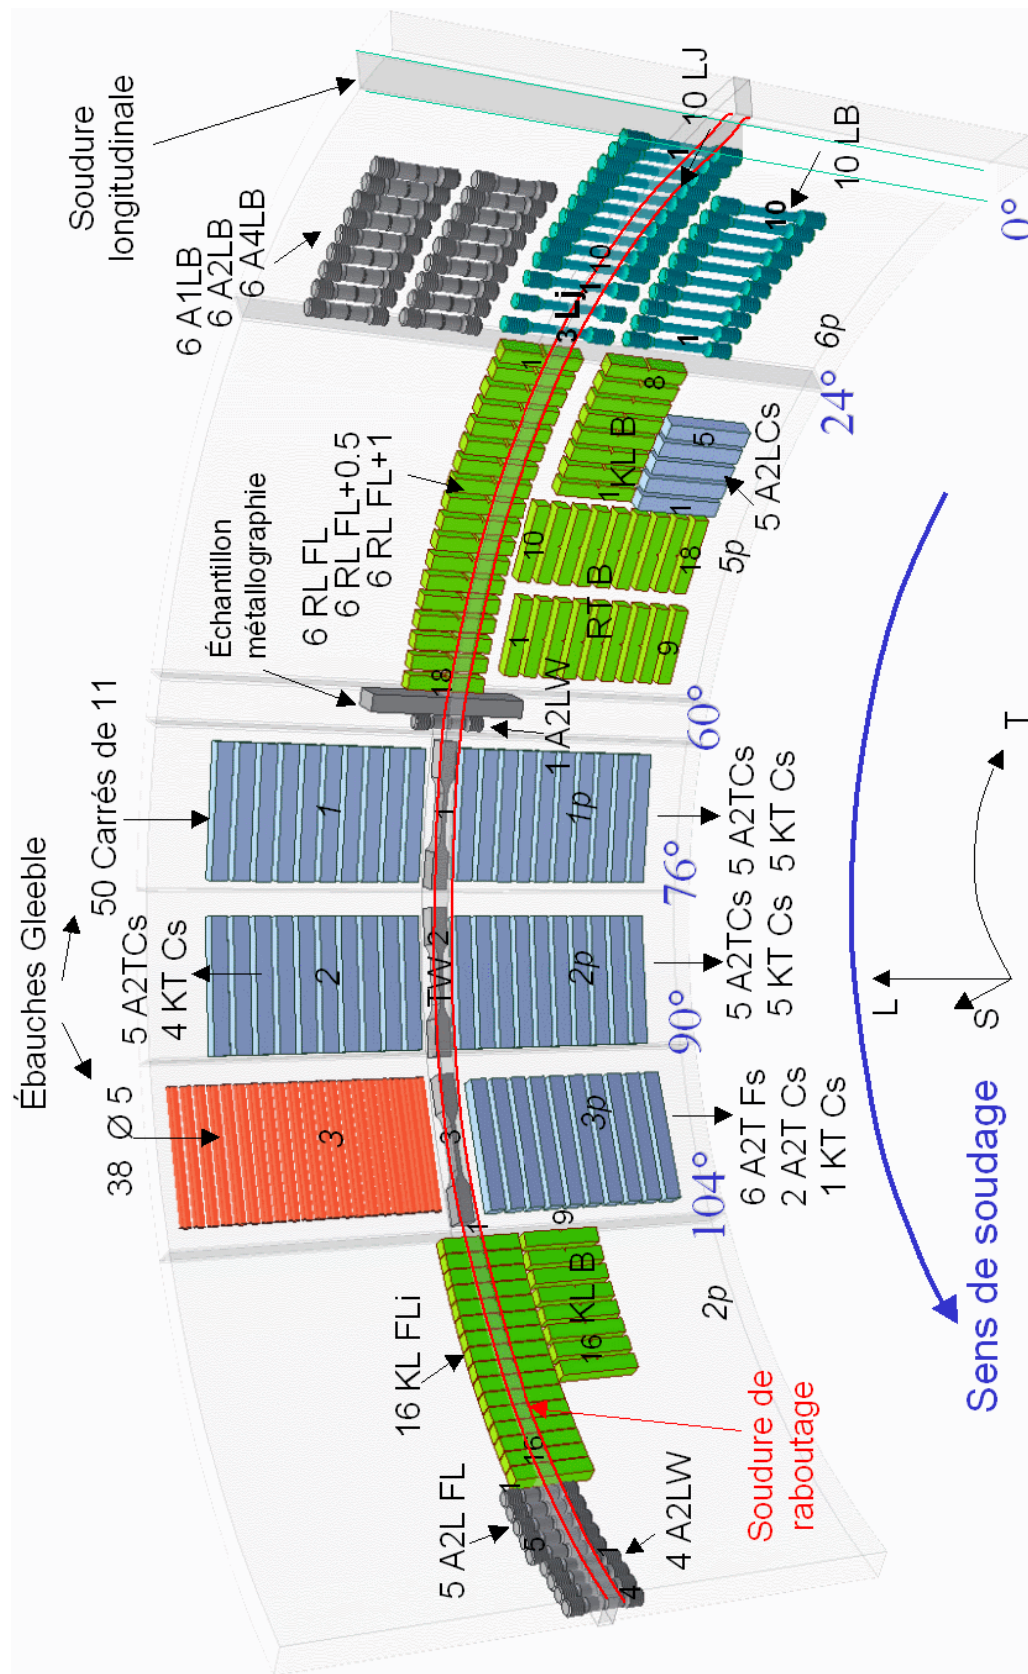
Plan de découpe de toutes les éprouvettes sur le tube 2B50 (Inventor®)
